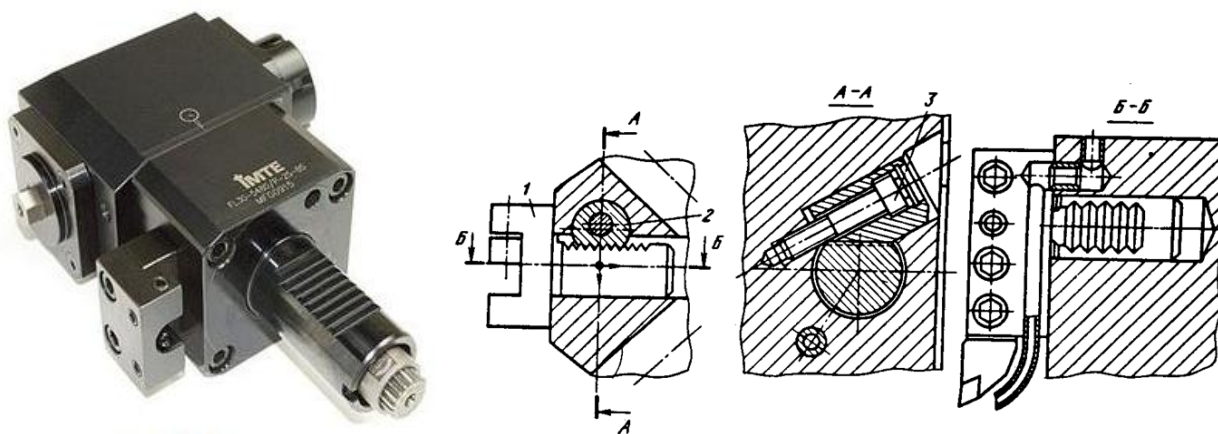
Инструментальный блок с системой крепления VDI
